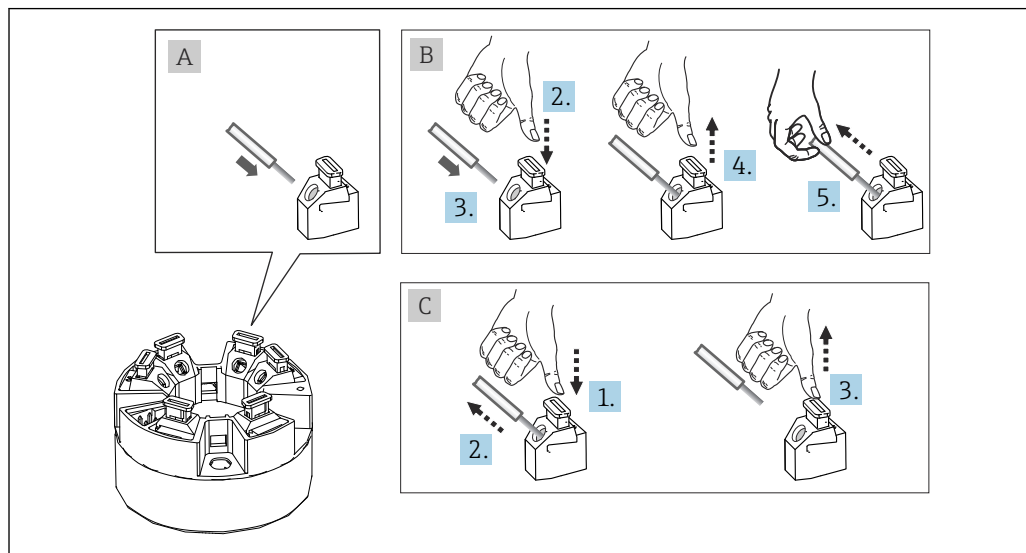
Conexão ao terminal de mola, usando o exemplo de um transmissor compacto
